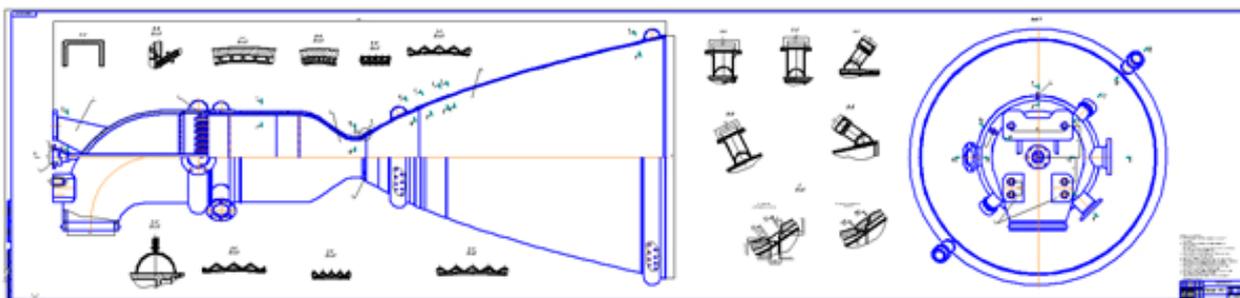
Сборочный чертеж камеры (Компас-3D v10)
